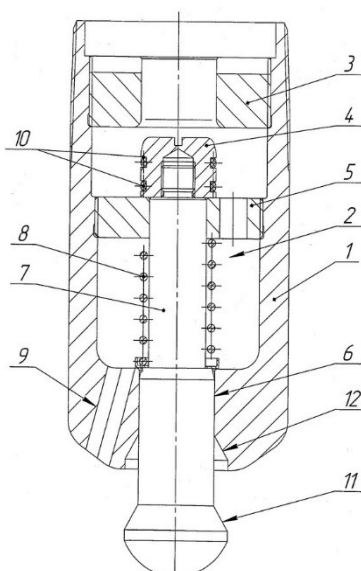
Башмак-клапан для хвостовика, где 1 – корпус, 2 – центральный проходной канал, 3 – седло, 4 – клапан, 5 – направляющая втулка, 6 – кольцевое сужение, 7 – толкатель, 8 – пружина, 9 – отверстия, 10 – уплотнительные резиновые кольца, 11 – конической поверхности, 12 – соответствующая поверхность корпуса
